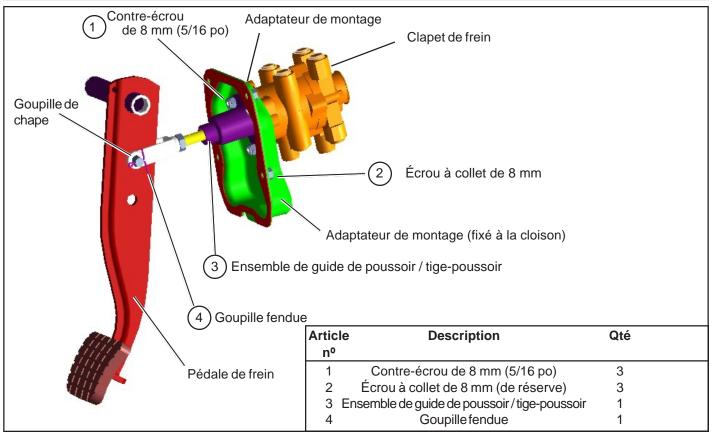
Ensemble de guide de poussoir / tige-poussoir
